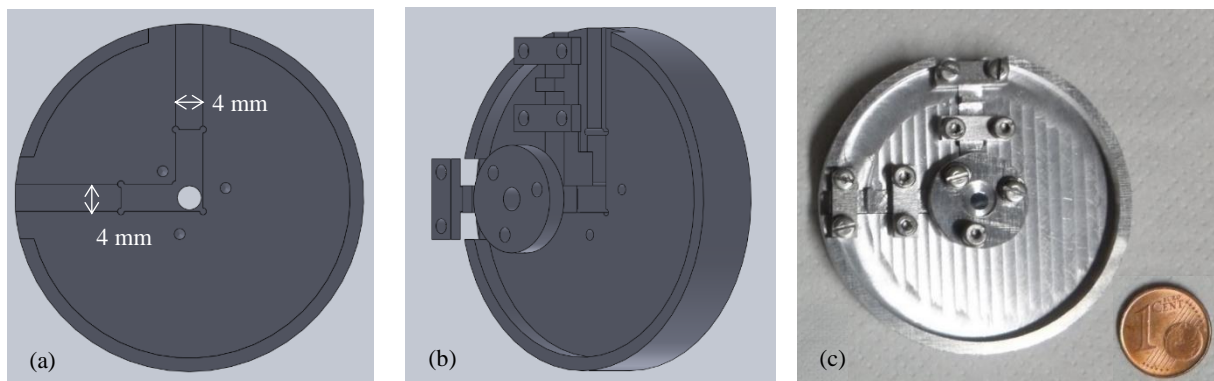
Suporte dos vidros de 4x4 mm² (meio ativo e espelho de saída): (a) desenho CAD da base do suporte; (b) vista explodida do desenho CAD dos suportes, com o sistema de 3 apertos; (c) suporte produzido em alumínio numa fresadora CNC.
